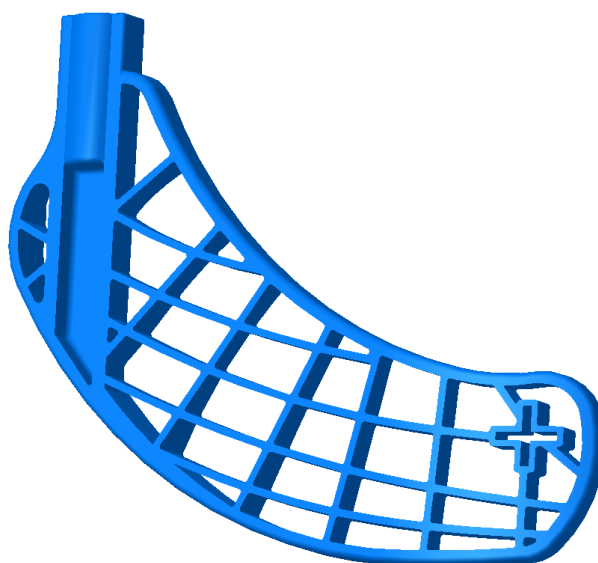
Detail vnitřní stěny a dvou drážek na čepeli
